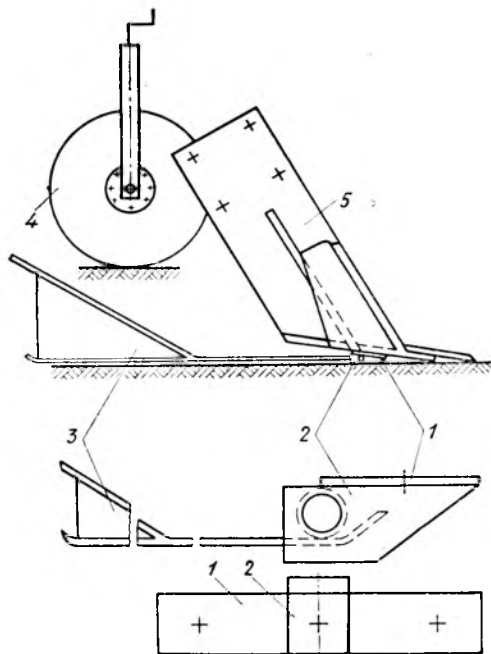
Приспособление для дополнительного рыхления почвы на рабочем органе выкопчного плуга ВПН-2:
